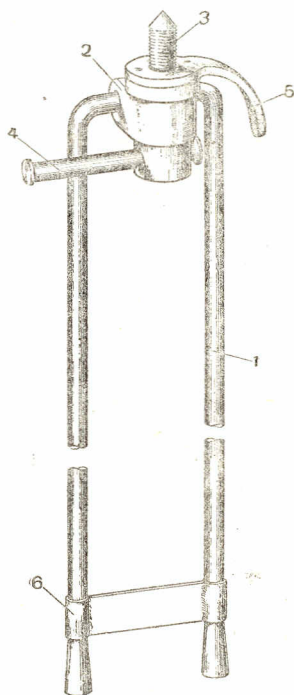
Вилка ветрянок (под держатель Дер-32).
